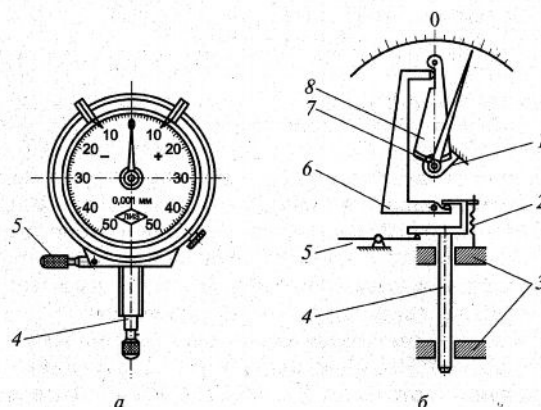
Рычажно-зубчатая измерительная головка (а) и ее схема (б): 1 - спиральная пружина; 2 - пружина; 3 - направляющие втулки; 4 - измерительный стержень; 5- арретир; 6 и 8 - рычаг; 7 - зубчатое колесо (триб)
